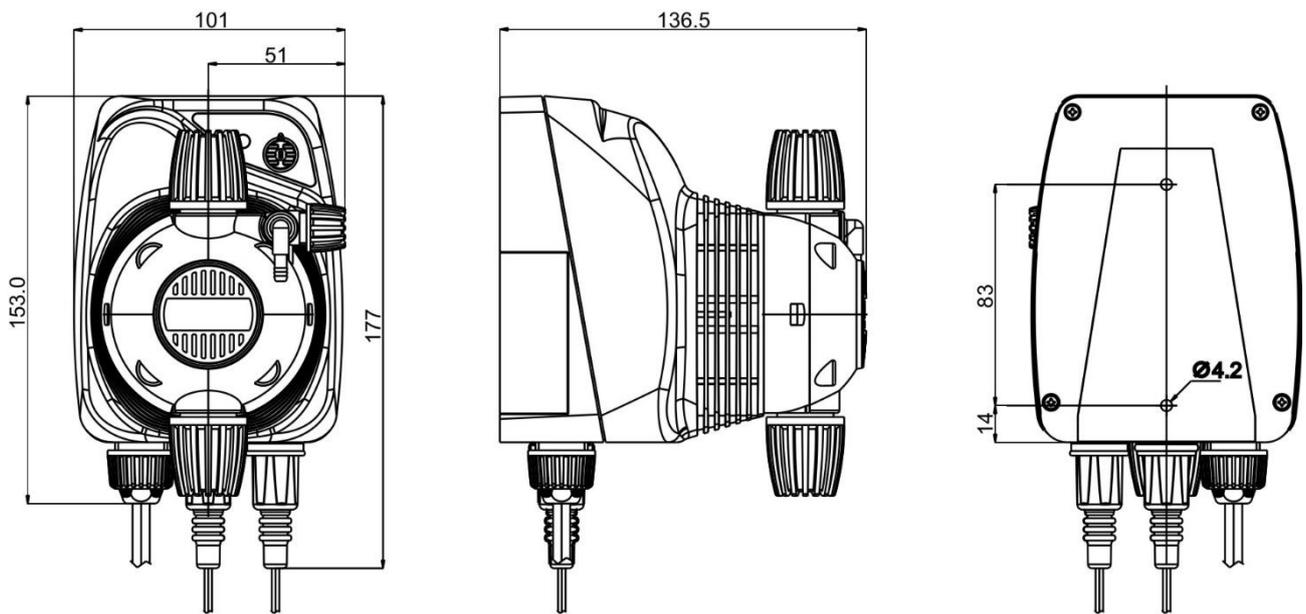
"HC150" A MURO – WALL MOUNTING – VERSION A PAROI – VERSION A PARED – WANDMONTAGE - НАСТЕННЫЙ
